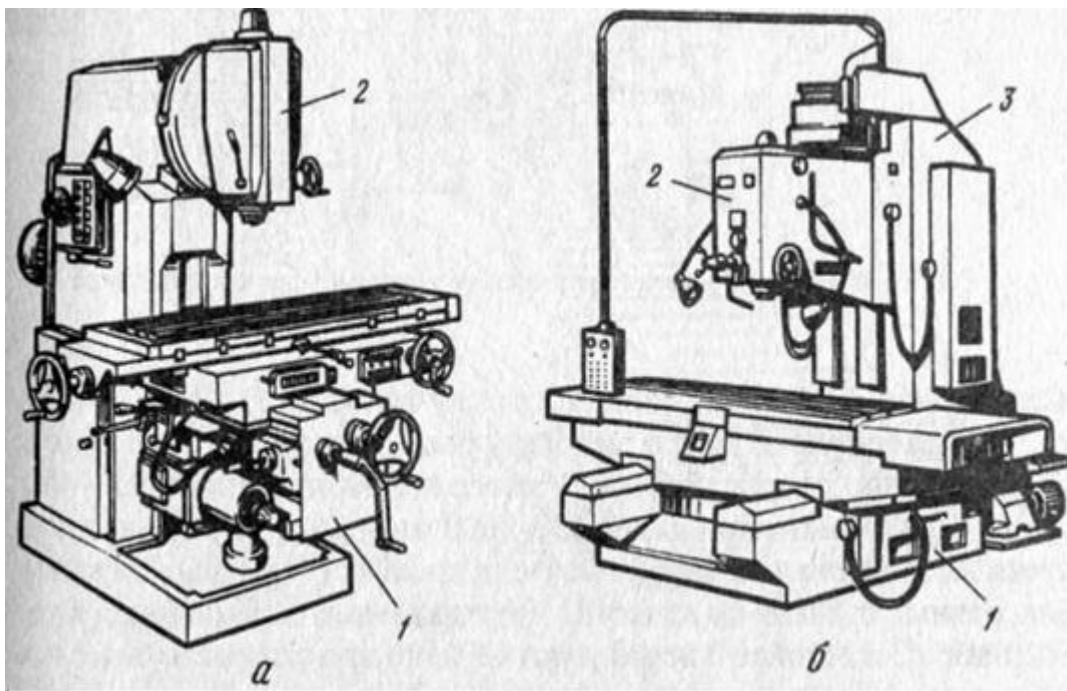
Вертикально-фрезерный станок: а – консольный, б - бесконсольный (с крестовым столом).
